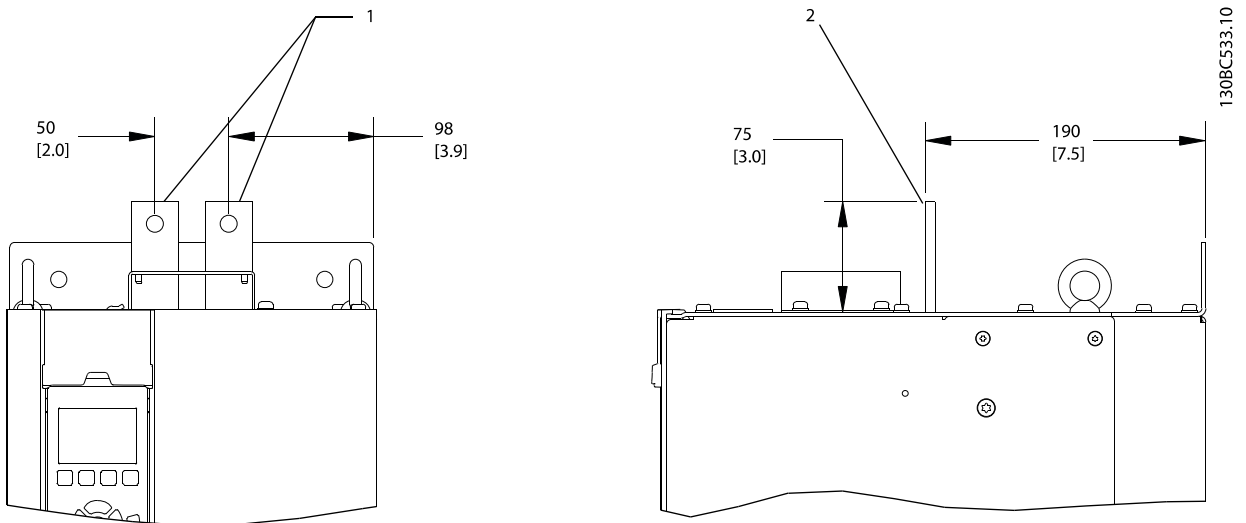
Terminais de regeneração e de distribuição da carga, D3h
